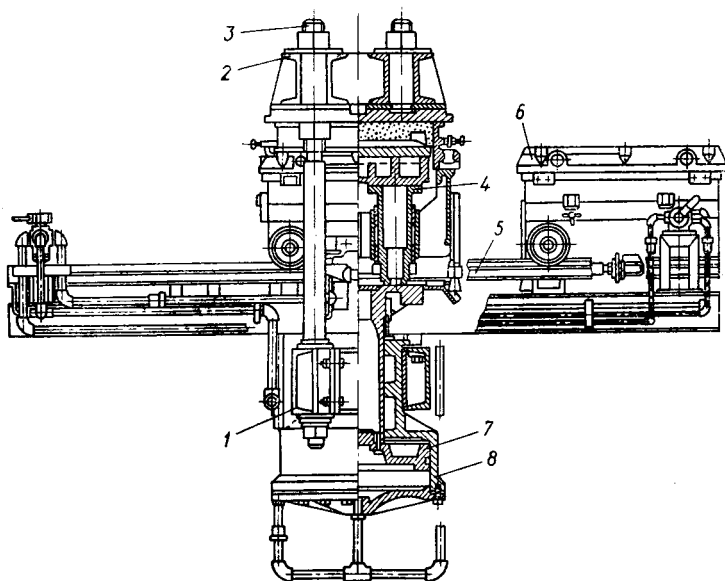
Общий вид прессовой формовочной машины ПФ-4
